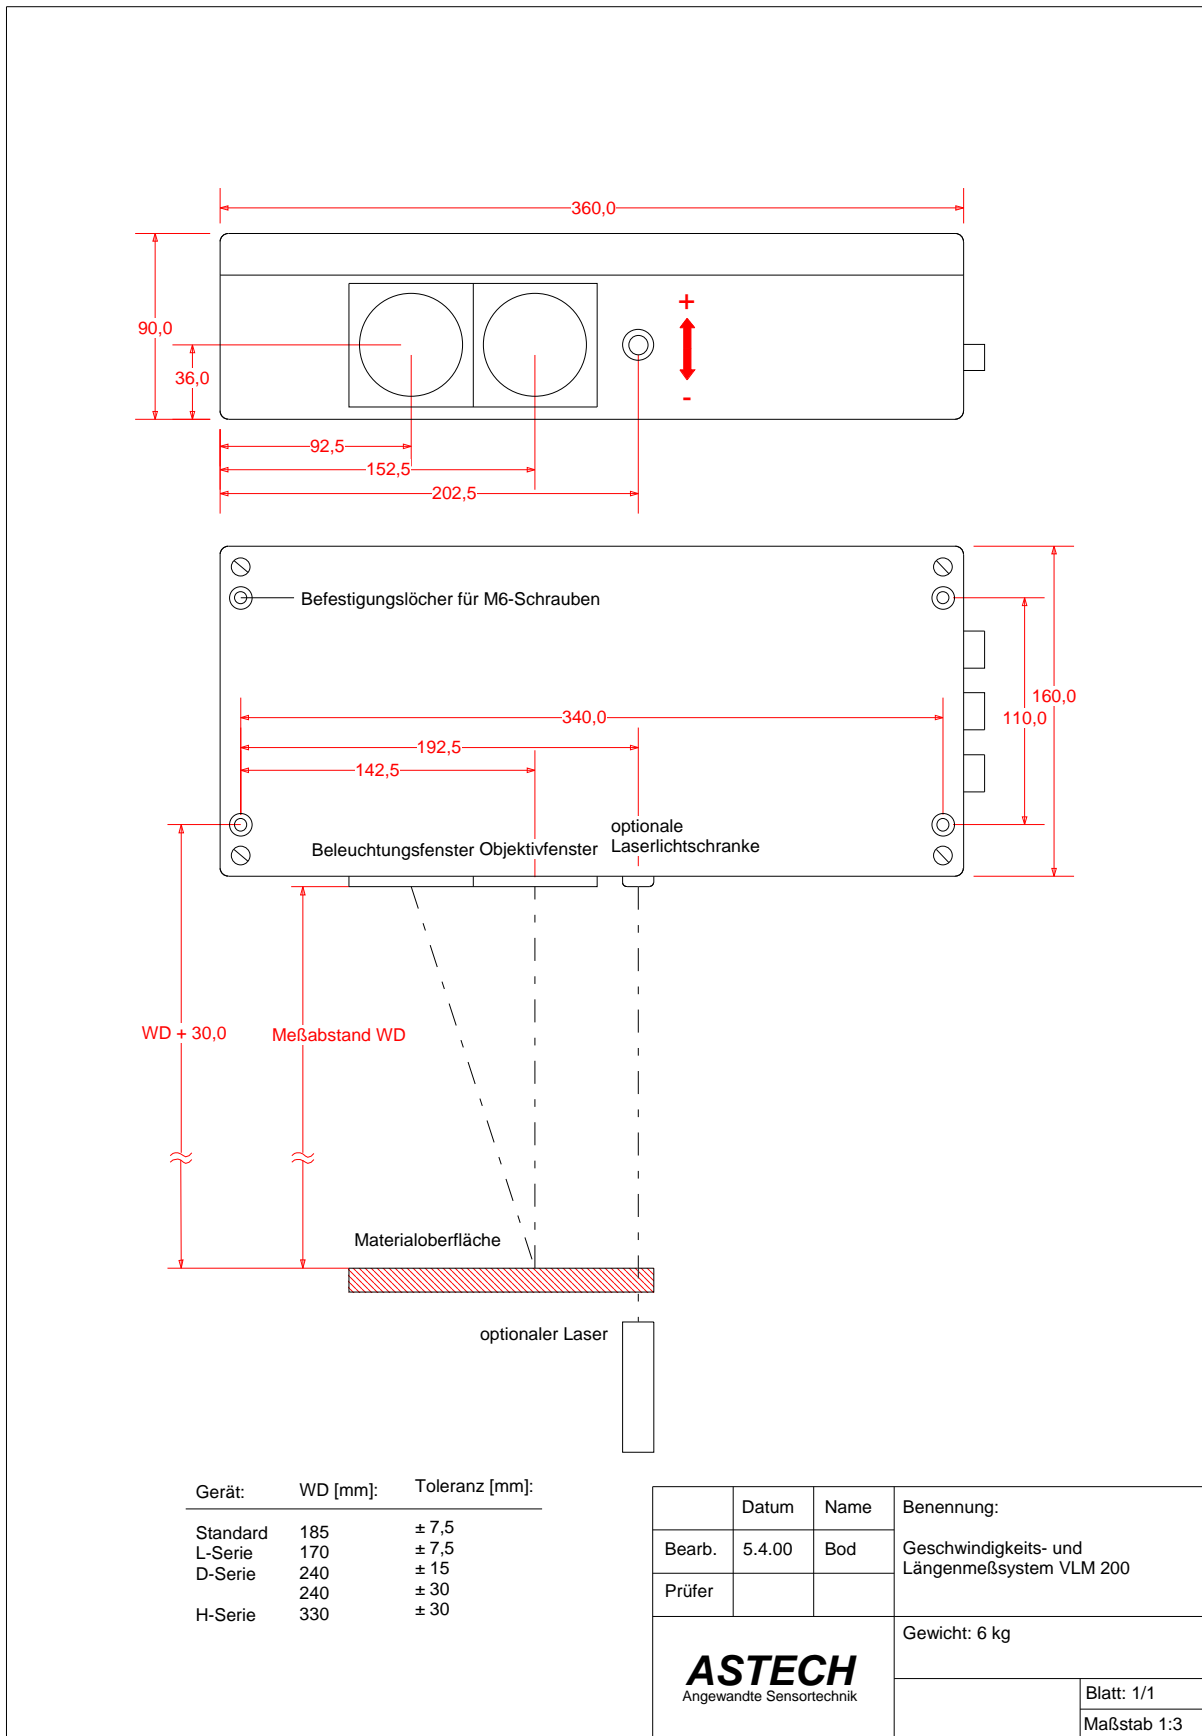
Maß- und Einbauzeichnung für verschiedene Ausführungen (n mm)
